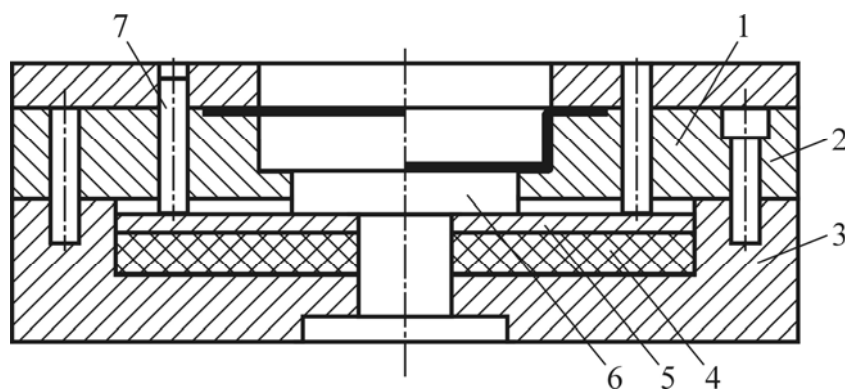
Конструктивная схема штампа со встроенным выталкивателем:
